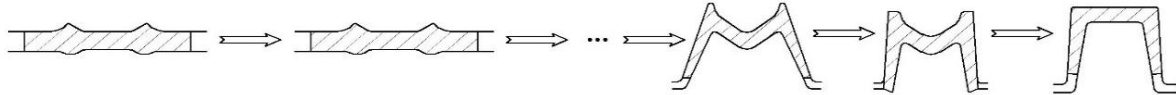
Схема швелерного калібрування прокатних валків за способом згинання
